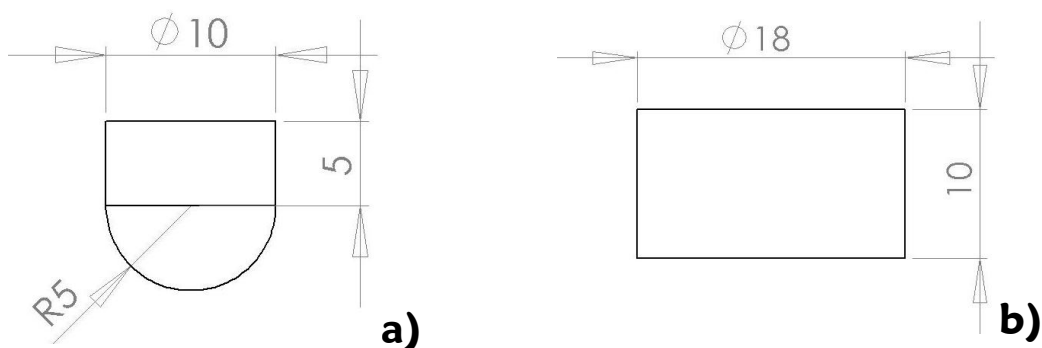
Dimensiones geométricas de pines y discos evaluados en desgaste (mm).
